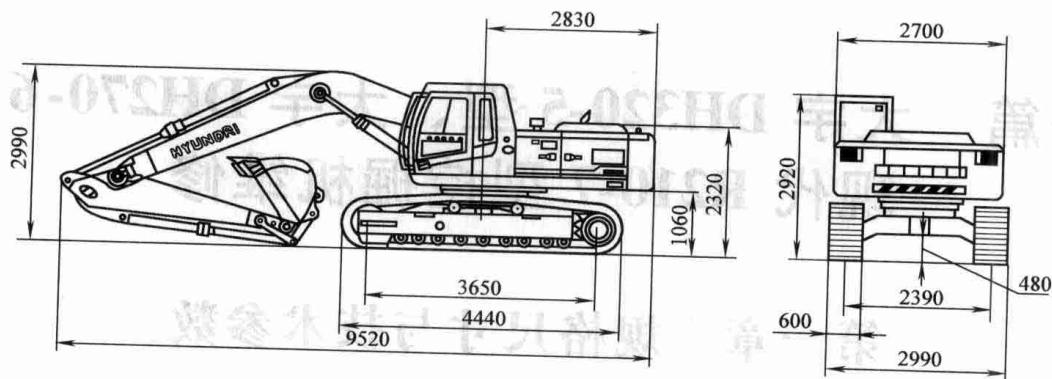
大宇 DH270-6 型挖掘机规格尺寸
